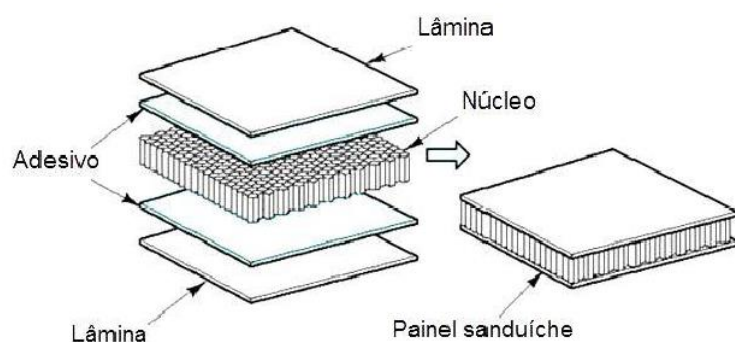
Pormenor construtivo do Painel tipo sanduiche
